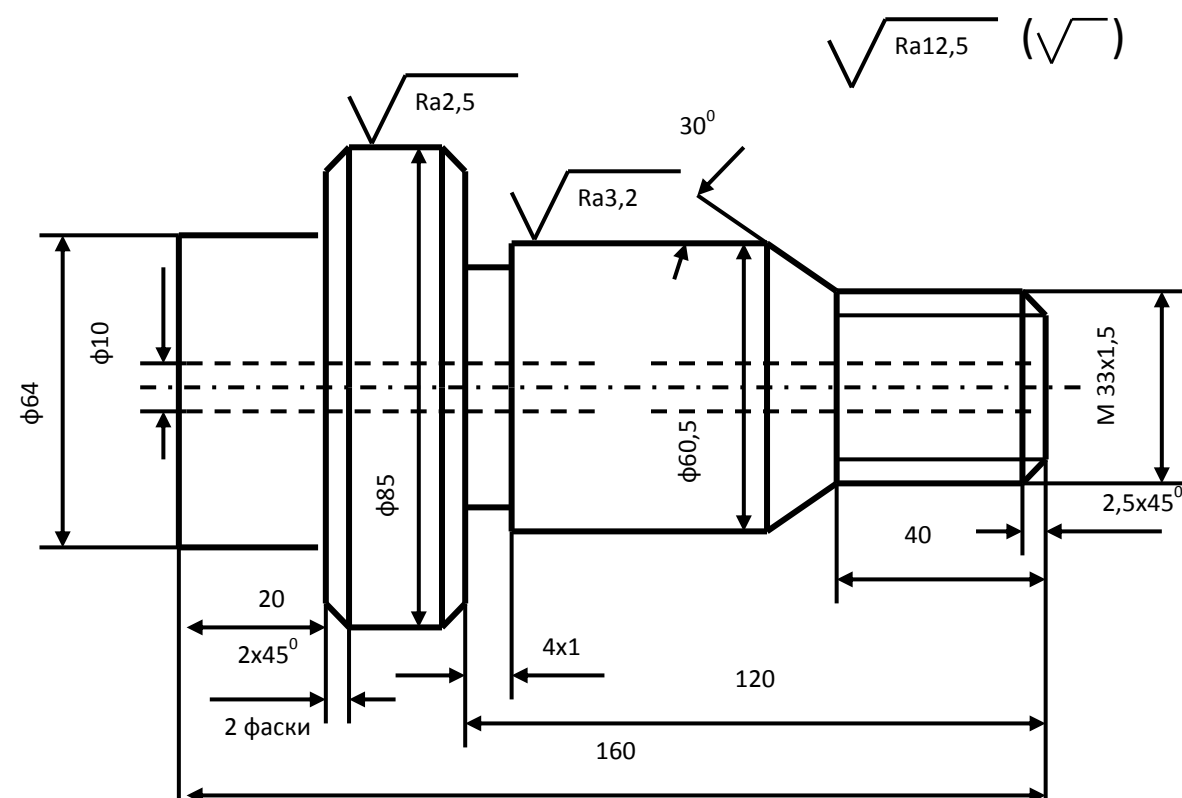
Чертеж токарной заготовки (оформляется на формате А4)
